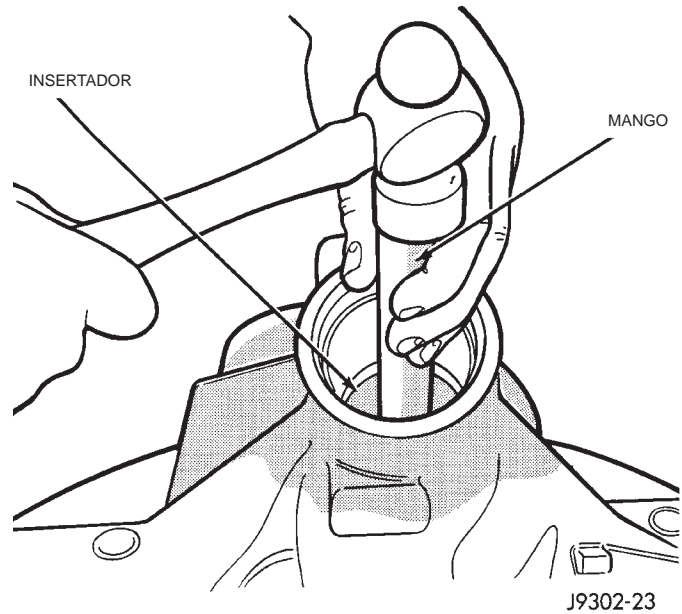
Desmontaje de la cubeta del cojinete trasero
